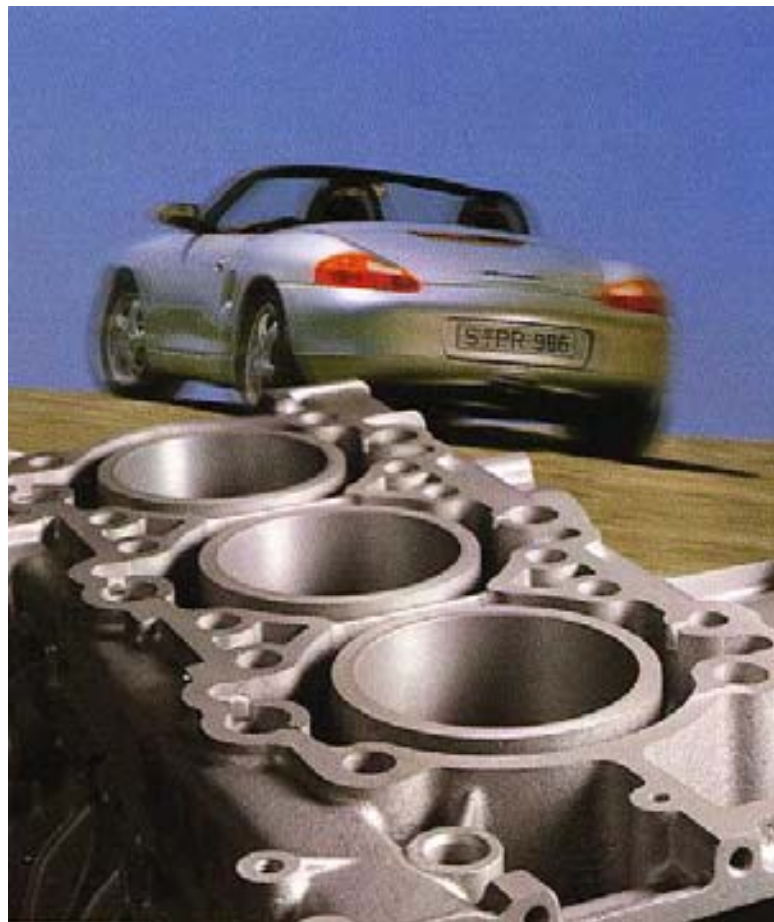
Eine neue Werkstoffklasse in Serie: Motorblock des Porsche Boxster mit MMC-Zylinderlauffläche.
